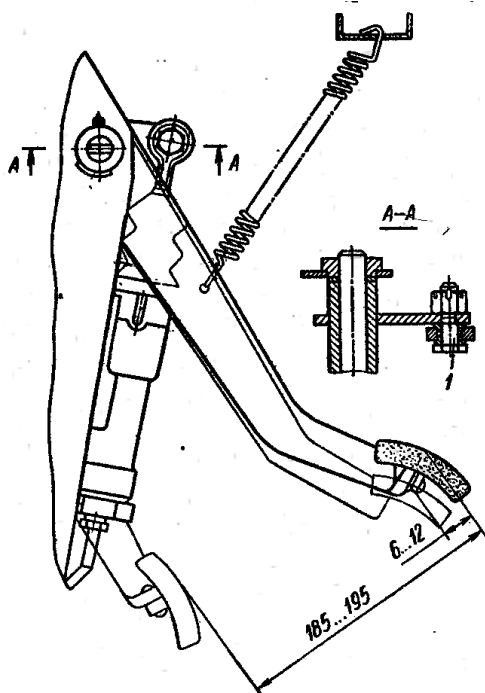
Регулировка свободного и полного хода педали сцепления
